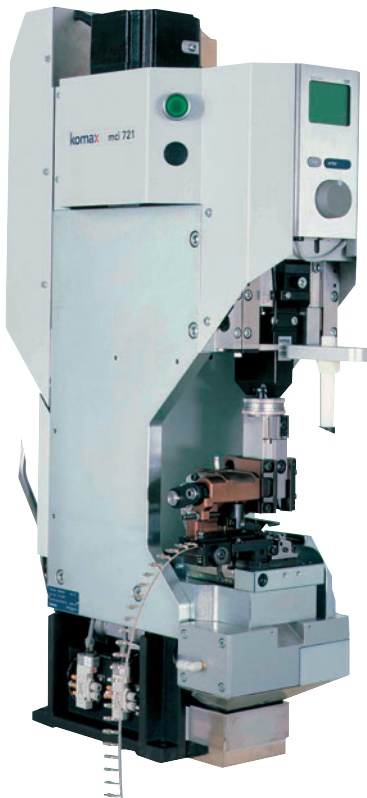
Bei allen Crimpungen wurde die Crimp-Kraft mit der CFA der Crimp-Pressse mci 721, Komax AG, Schweiz, aufgenommen
